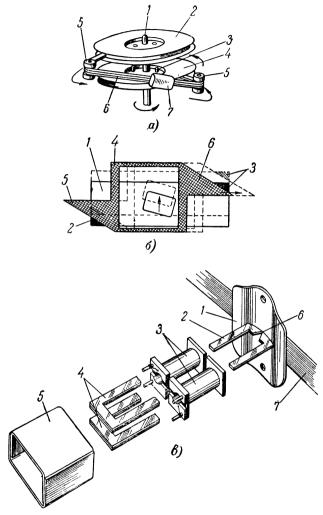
Устройство блока кассет (a), механизма смещения магнитной головки (б) и магнитной головки магнитофона "Говорящая книга" (в).
